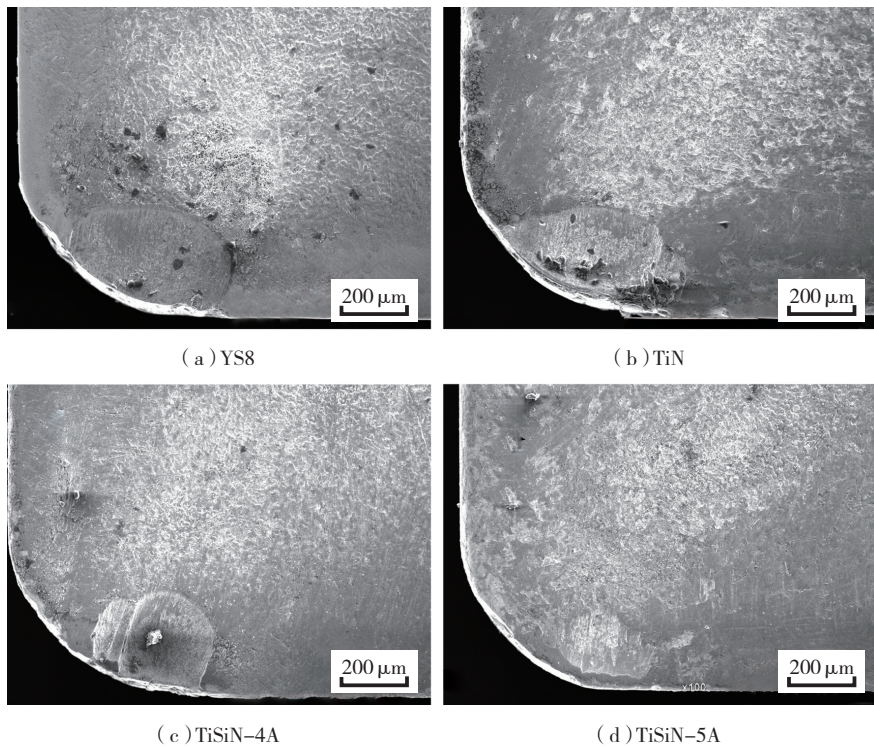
4种刀具在切削距离1200m时前刀面磨损形貌
